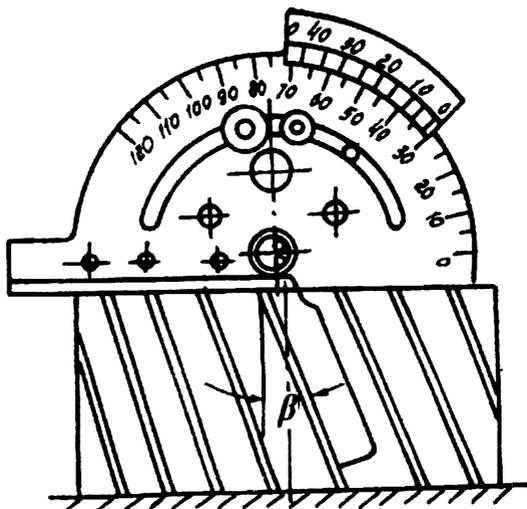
Измерение наклона спирали цилиндрической фрезы β с помощью универсального угломера
